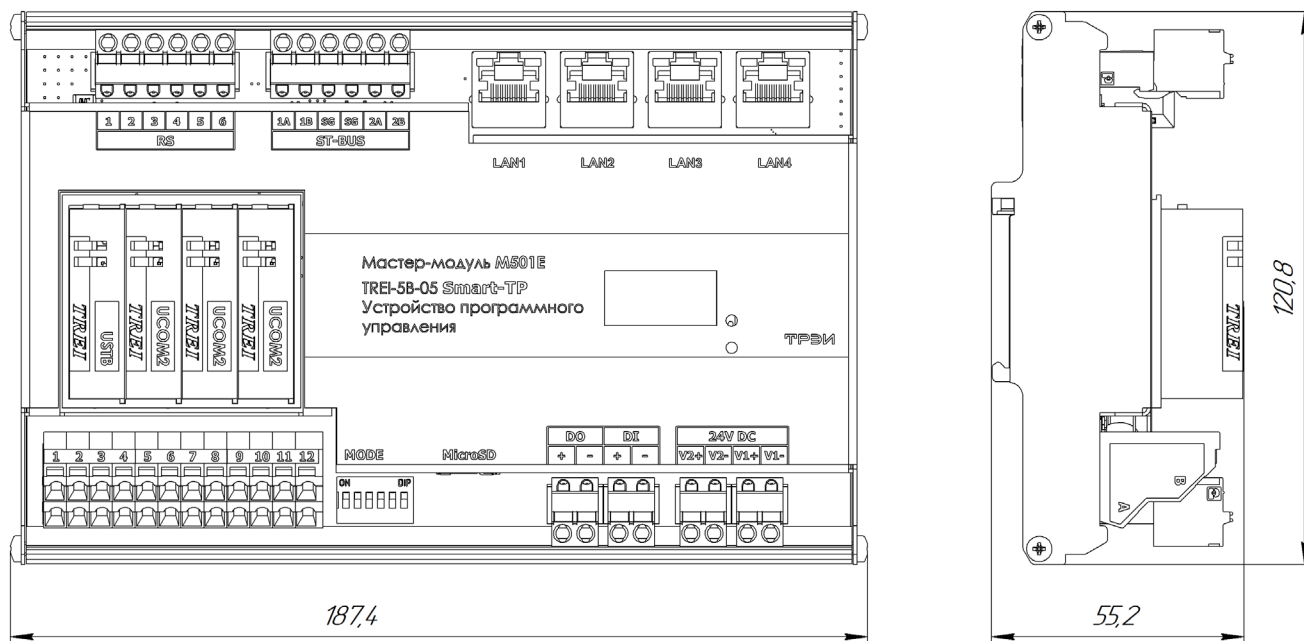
Чертеж общего вида M501E с указанием габаритных и присоединительных размеров
